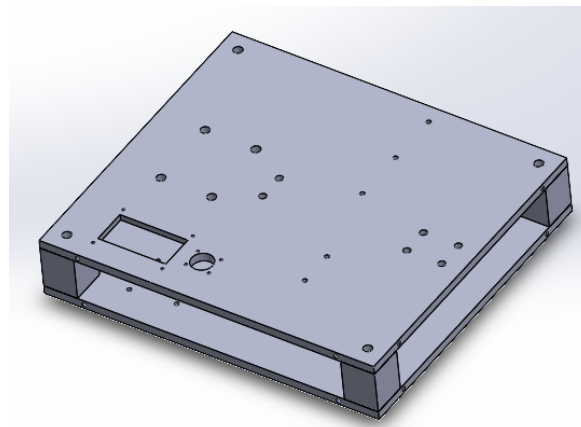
Montaggio piastra superiore e inferiore ai blocchetti
